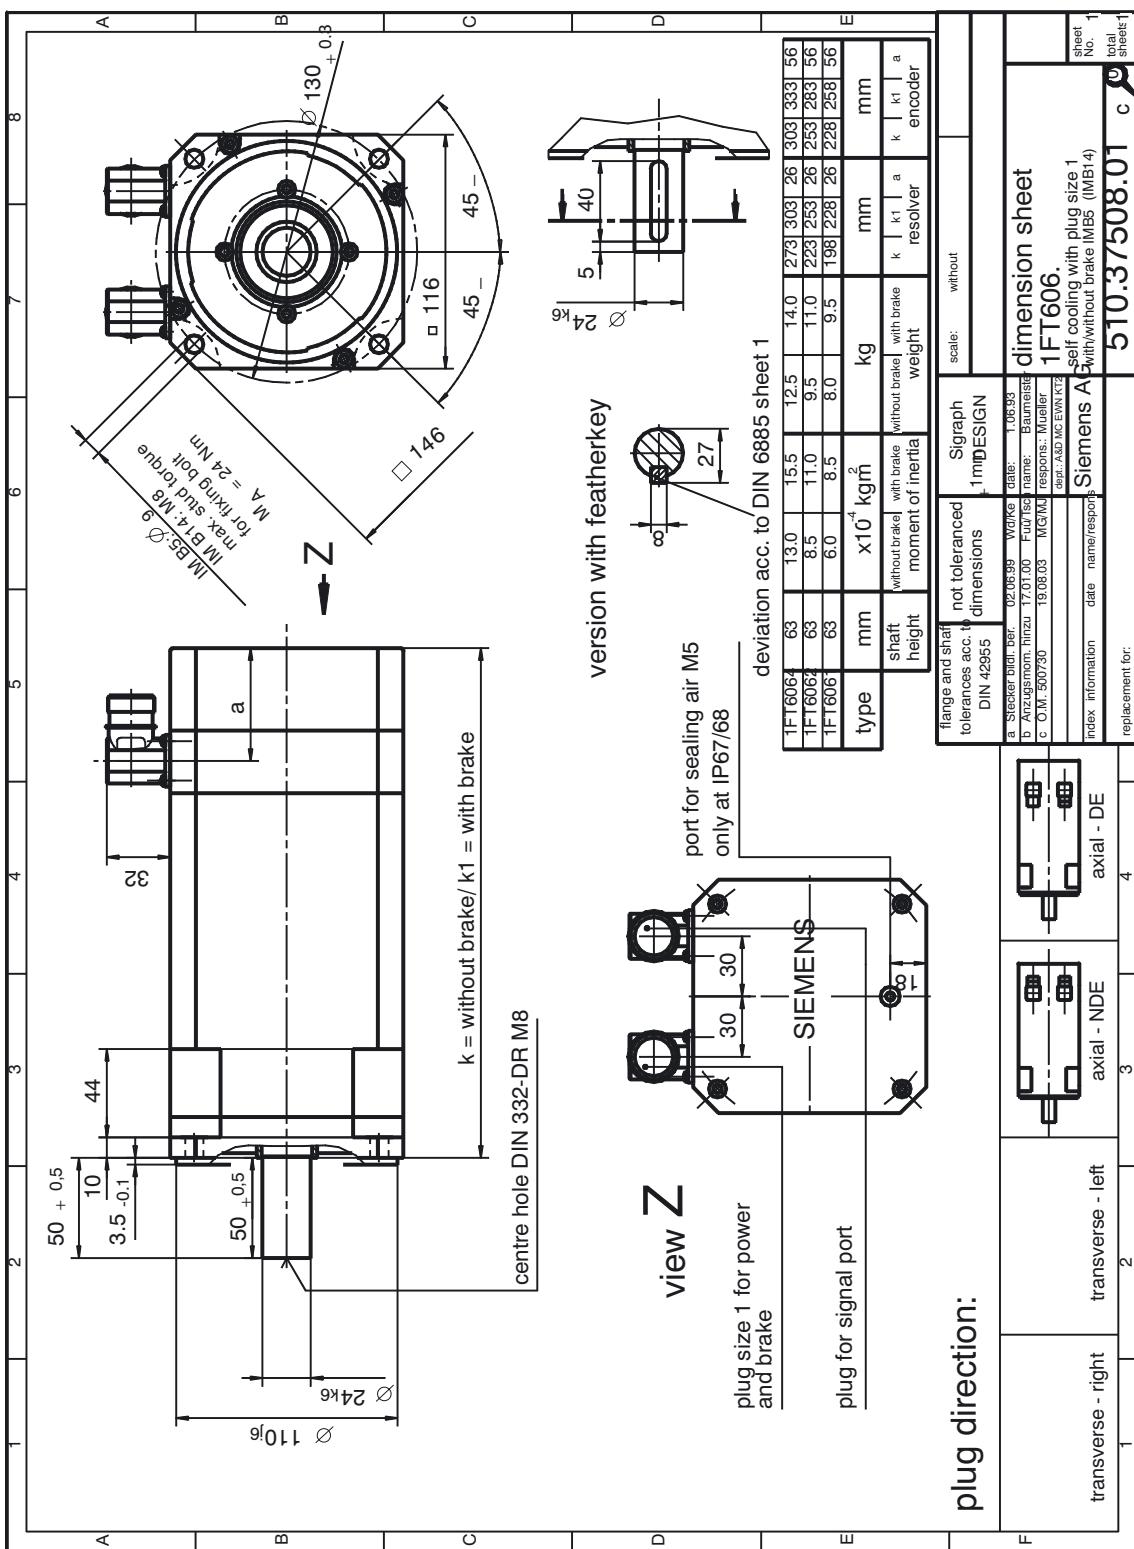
1FT606□ selbstgekühlt mit Stecker Größe 1
